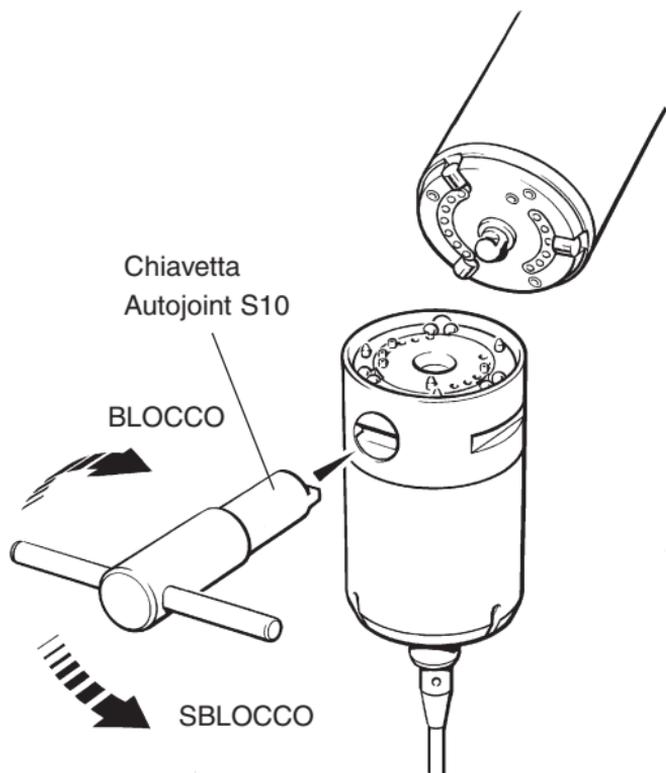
Montaggio sulla testina di una sonda con Autojoint
